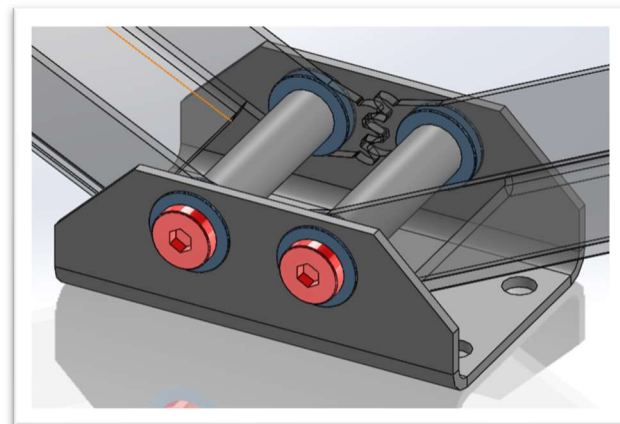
Soporte de elevador. Fuente: Elaboración propia
